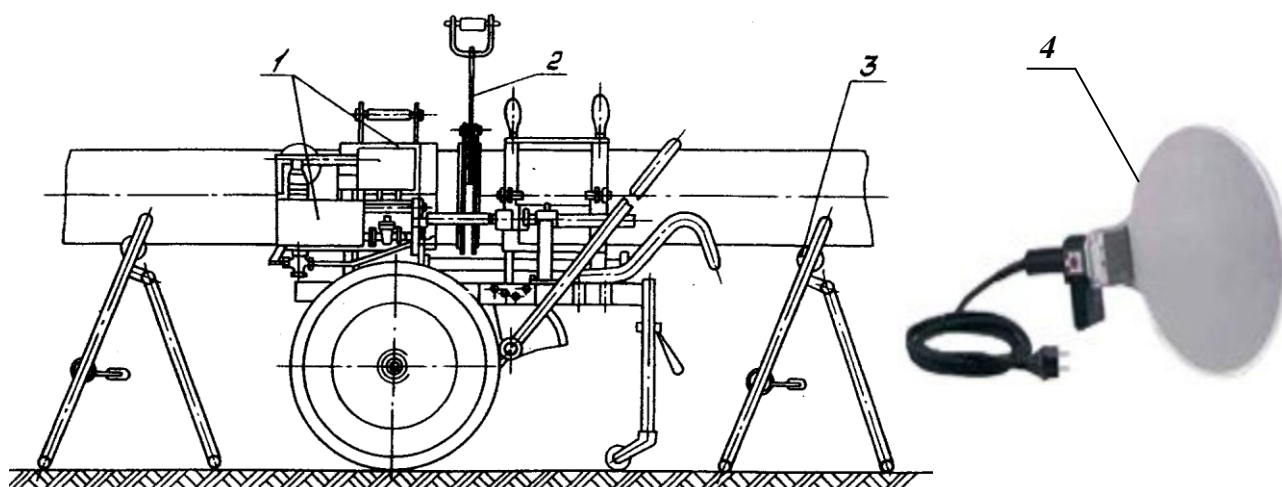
Установка мобильная для сварки полиэтиленовых труб малого диаметра УСПТ-09: 1 – блок сварочный; 2 – устройство торцовочное; 3 – опора; 4 – нагреватель
